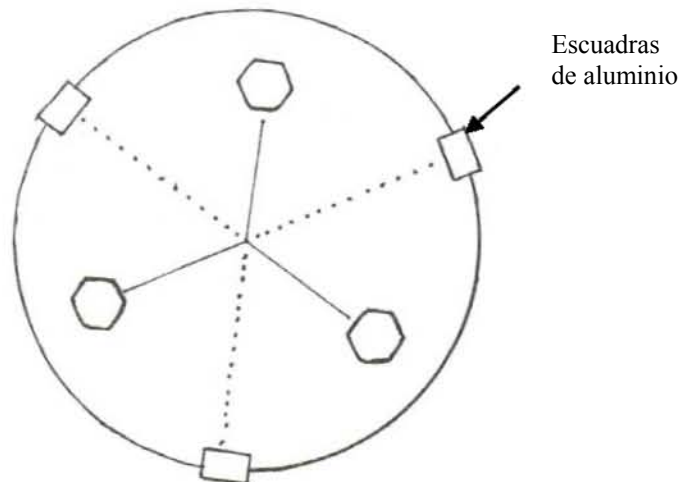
En la tapa pequeña se encuentra la cabeza hexagonal del tornillo y las escuadras de aluminio.
